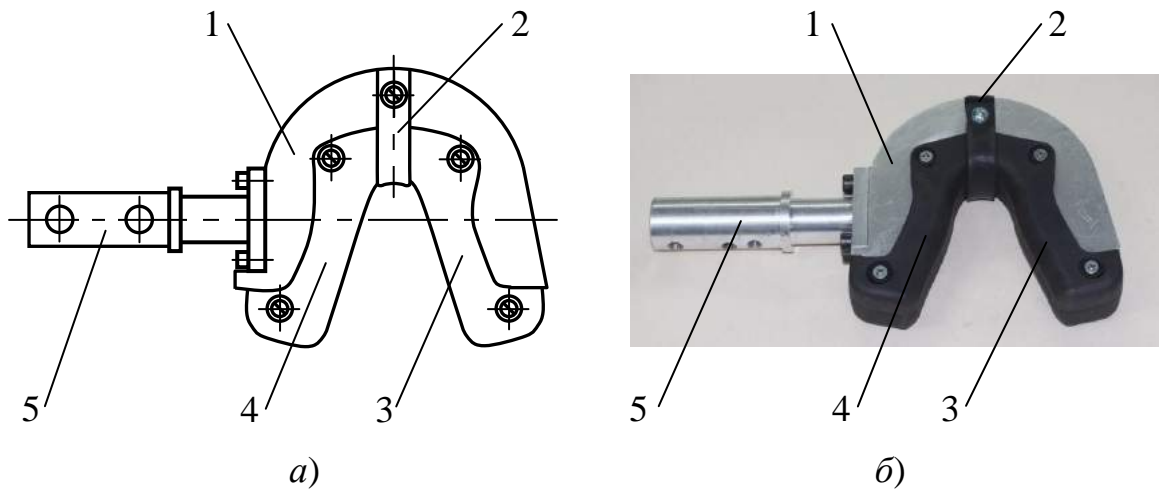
Вилчастий захват (*a* – схема; *б* – загальний вигляд):
